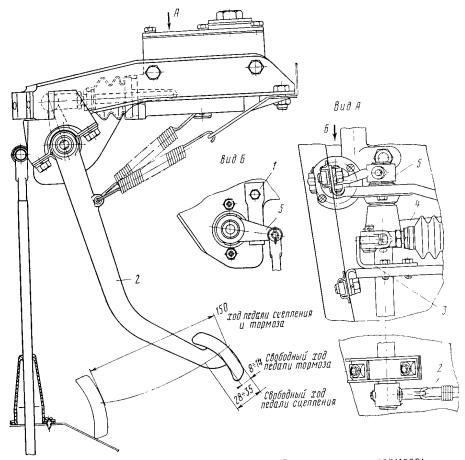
Регулировка положения педалей сцепления и тормоза: 1 — упорный кронштейн педали сцепления; 2 — педаль сцепления; 3 — упорный кронштейн педали тормоза; 4 — педаль тормоза; 5 — рычаг выключения сцепления
